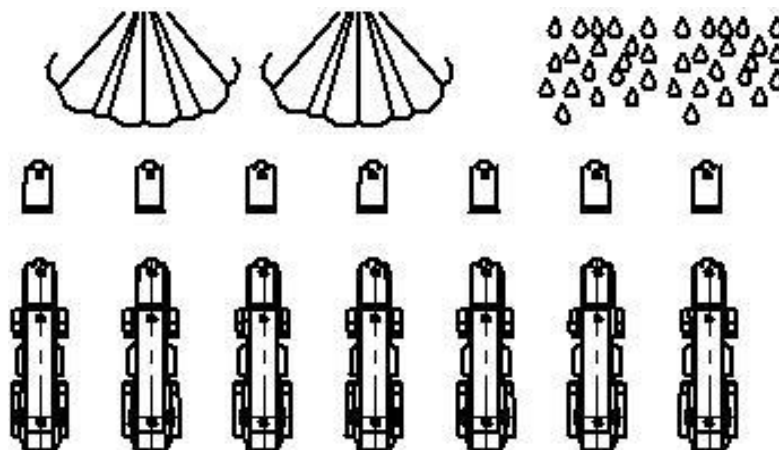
Подготовка деталей к сварке
